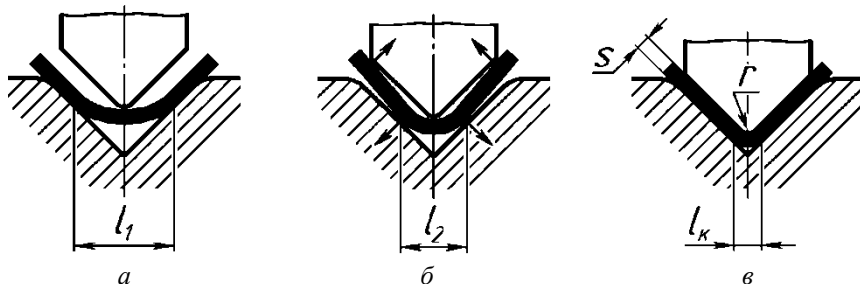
Контакт заготовки с инструментом в ходе одноугловой гибки:
